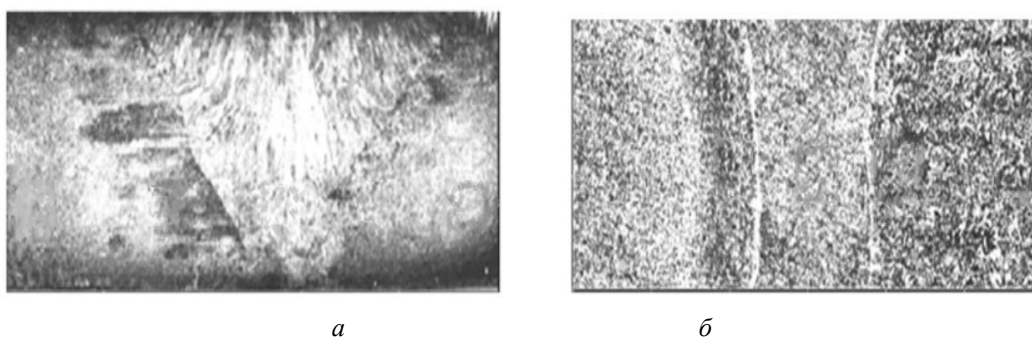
Микрошлифы сварных швов: а) дуговая сварка; б) лазерная сварка
